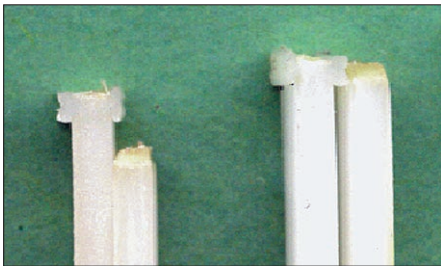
Bruchbild Schweißung Serie 2, HS-IR-d, Suspensionstyp
